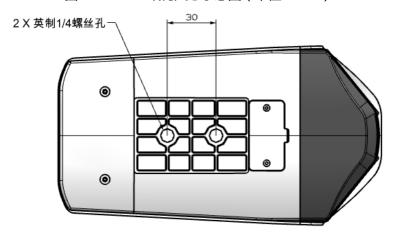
A1B 底部螺丝孔示意图 (单位:mm)
